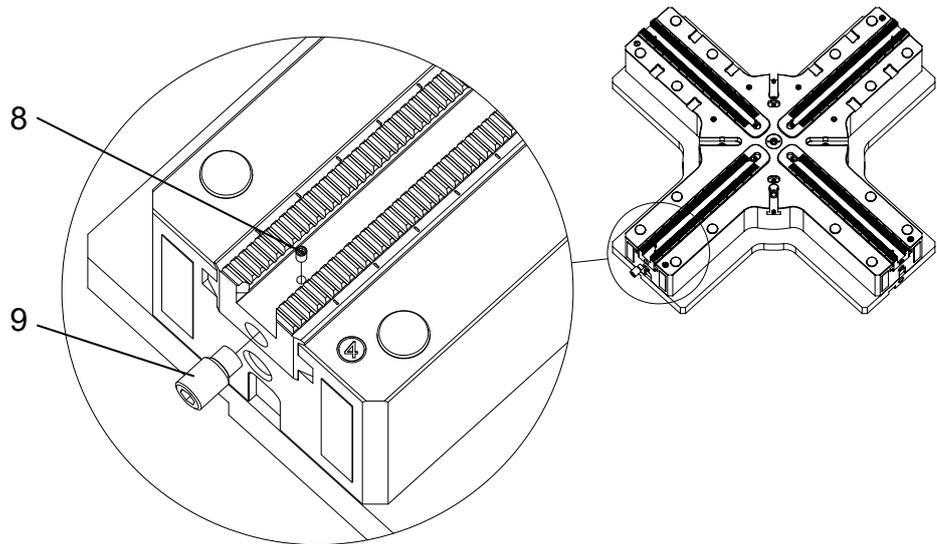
Entfernen der Gewindestifte des InoFlex® VL100
